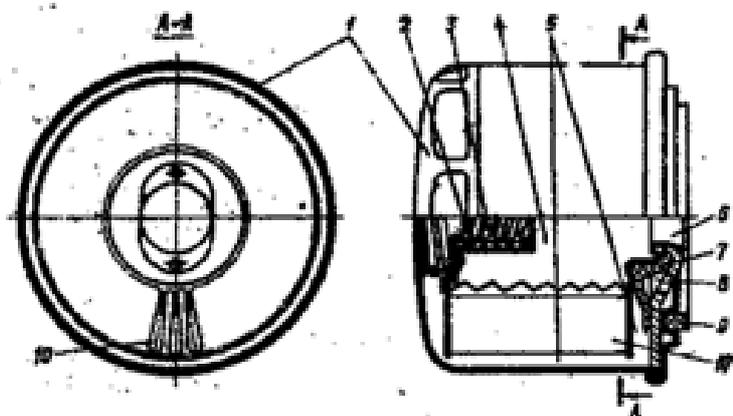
Масляный фильтр: 1 - корпус фильтра; 2 - перепускной клапан; 3 - пружина перепускного клапана; 4 - центральная полость; 5 - наружная полость; 6 - резьбовое отверстие; 7 - противодренажный клапан; 8 - впускные отверстия; 9 - прокладка фильтра; 10 - фильтрующий элемент
